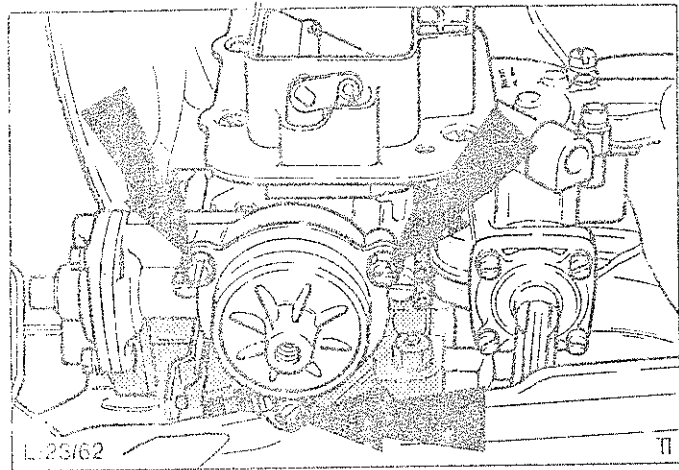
Befestigungsschrauben - Thermofedergehäuse (Wassergehäuse - Startautomatik zur Verdeutlichung abgebaut)
